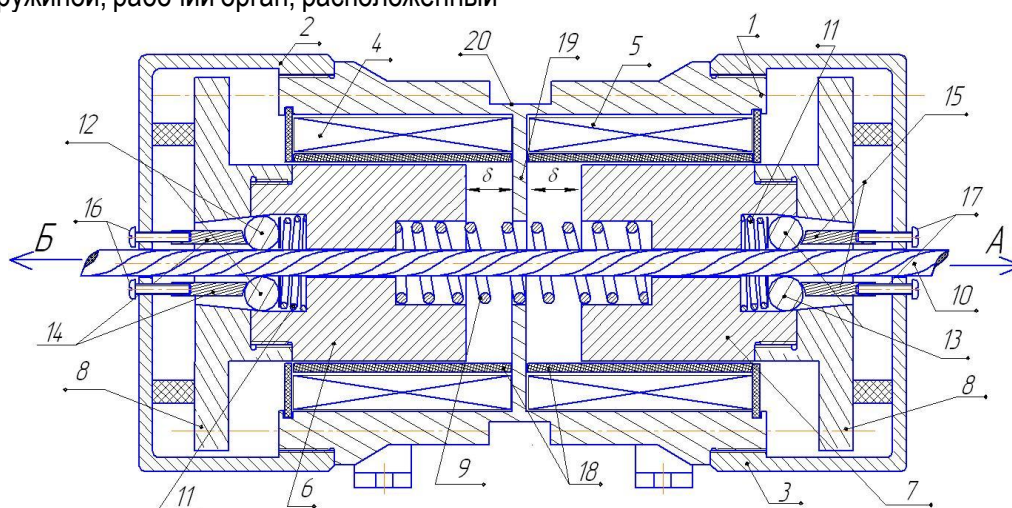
Реверсивный линейный электромагнитный двигатель
